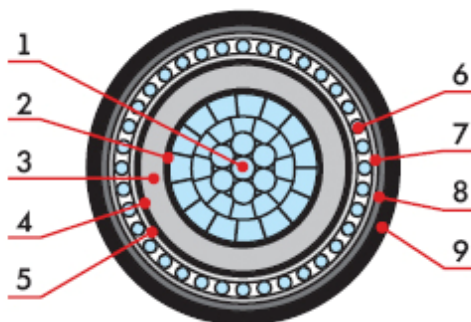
Конструкция одножильного кабеля на напряжение 10-35 кВ:
